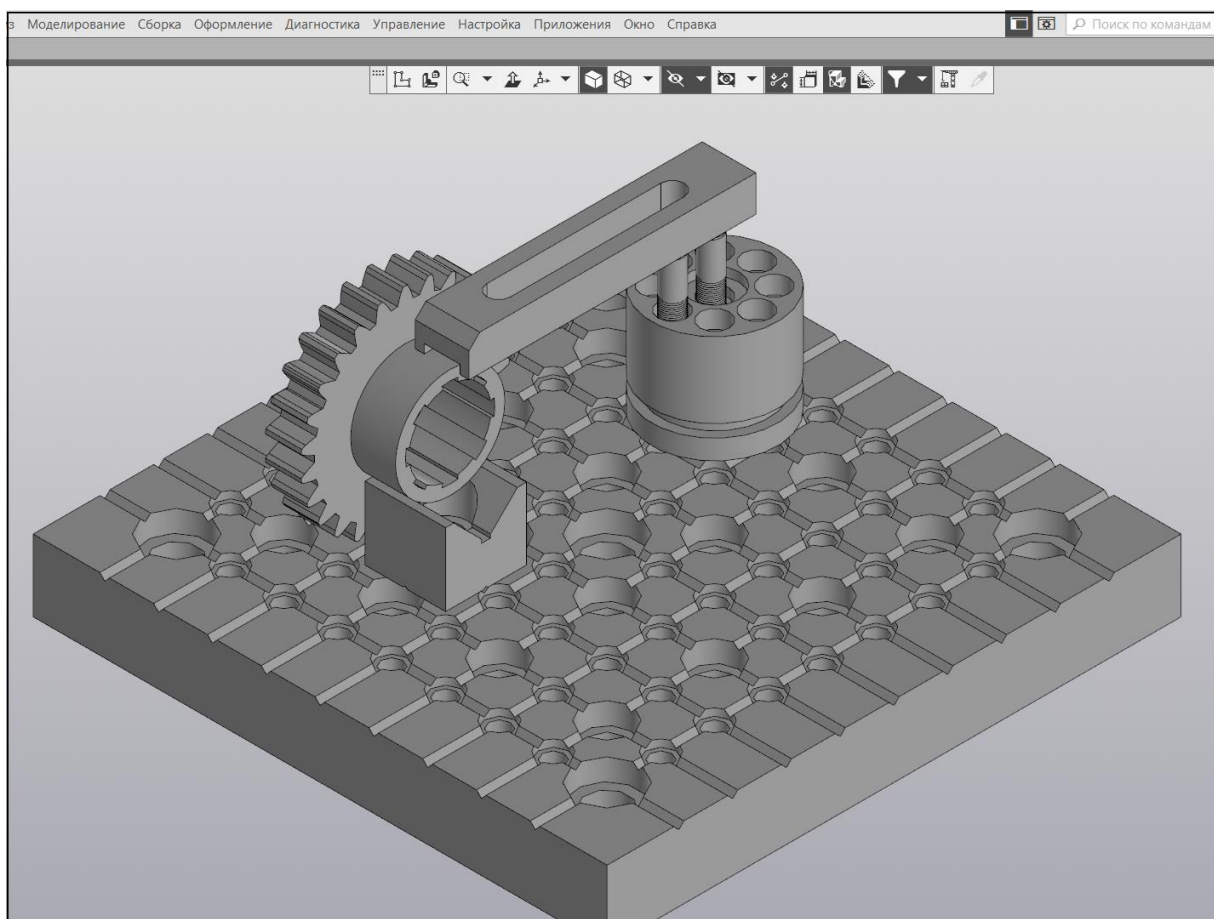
сборка УСПО для детали типа «Шестерня»
